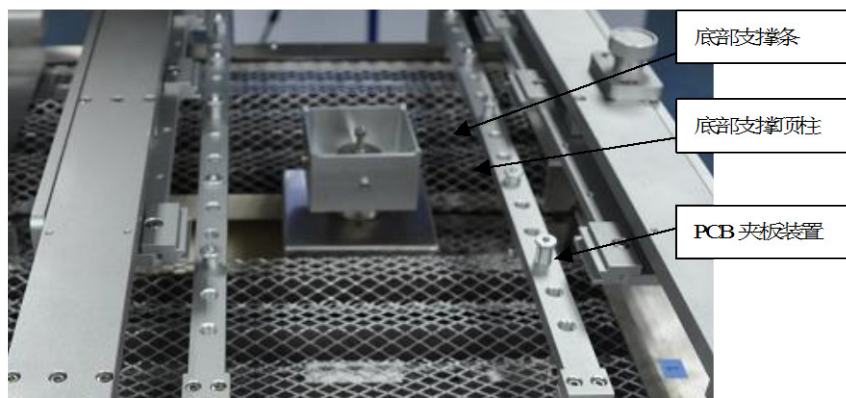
PCB 夹板装置和 PCB 底部支撑条
